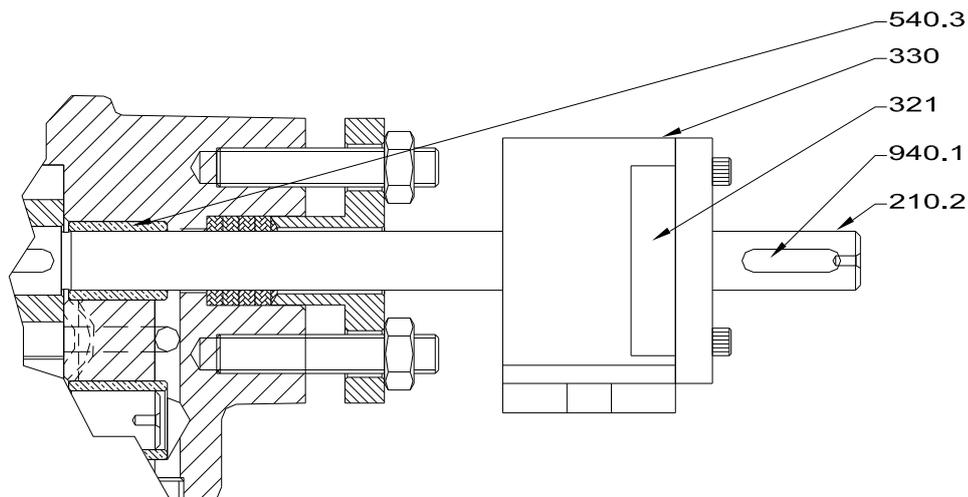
Desenho em Corte bomba FBE c/ Mancal Externo
